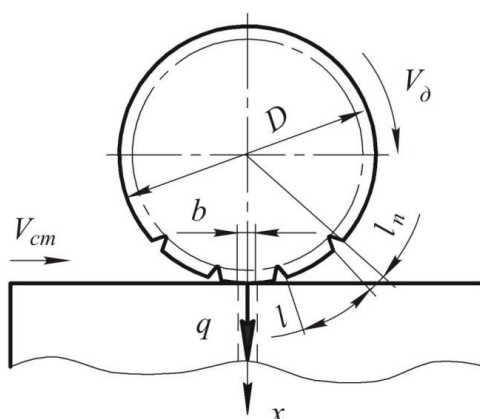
Схема фрикційного зміцнення деталей машин інструментом з перервною робочою частиною.
